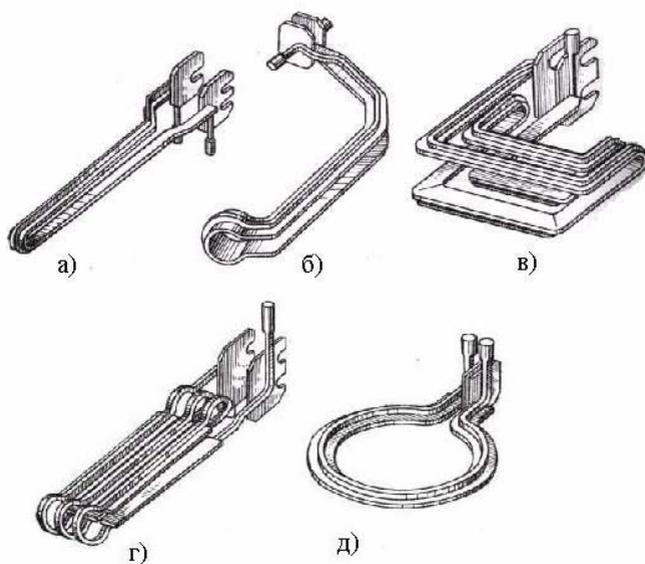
Индукторы для наплавки различных деталей машин:
